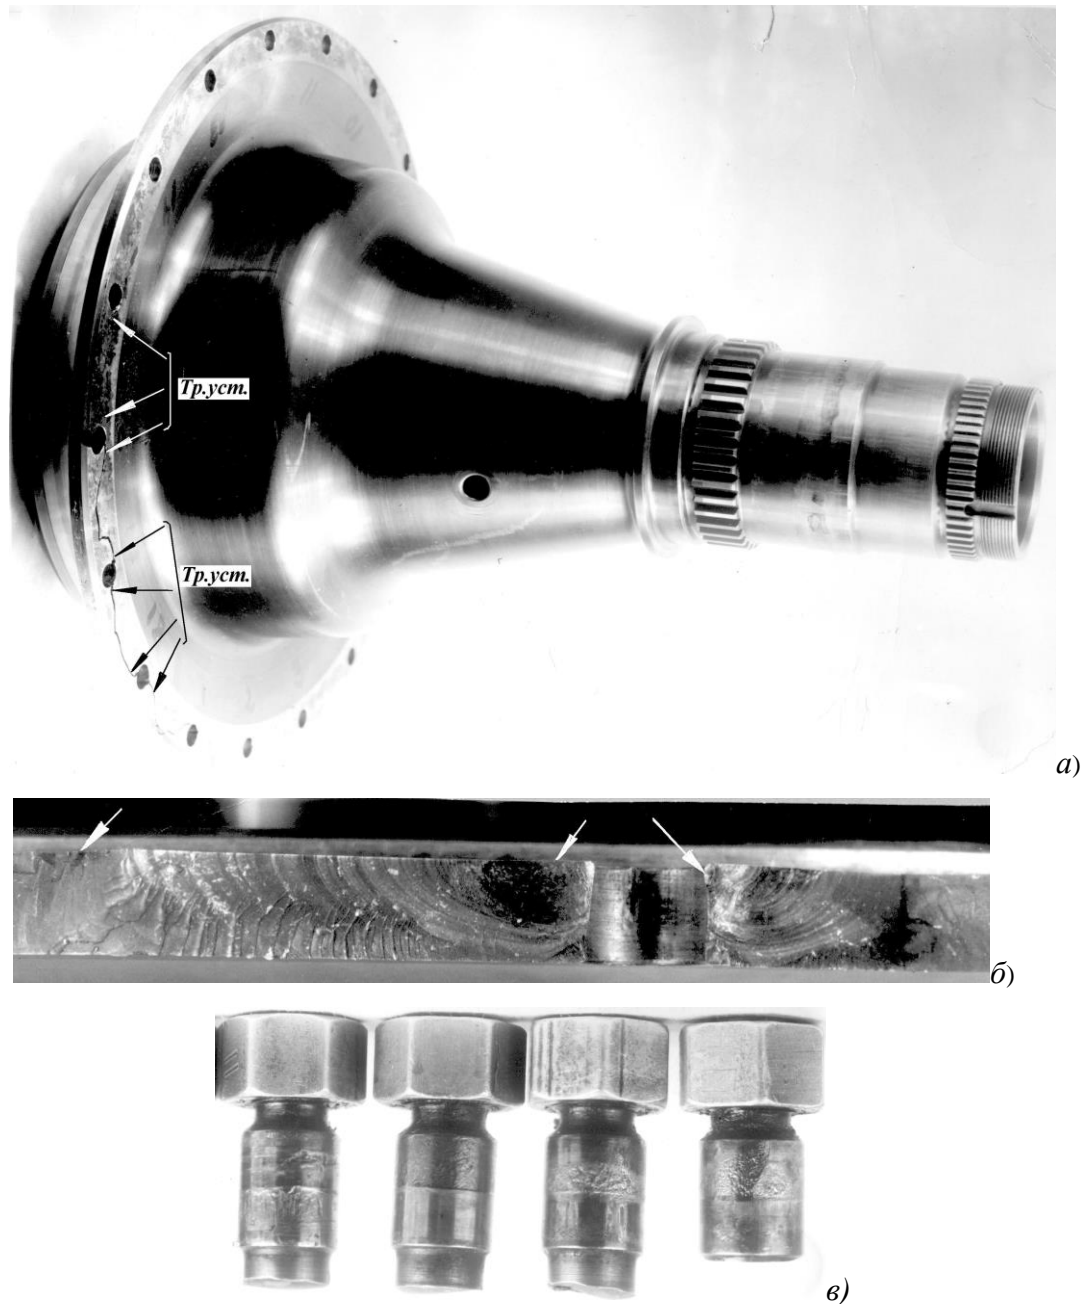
Разрушение вала-шестерни по фланцу в зоне болтовых соединений с шестерней от фреттинг-усталости (стрелками указаны очаги усталостных разрушений):
